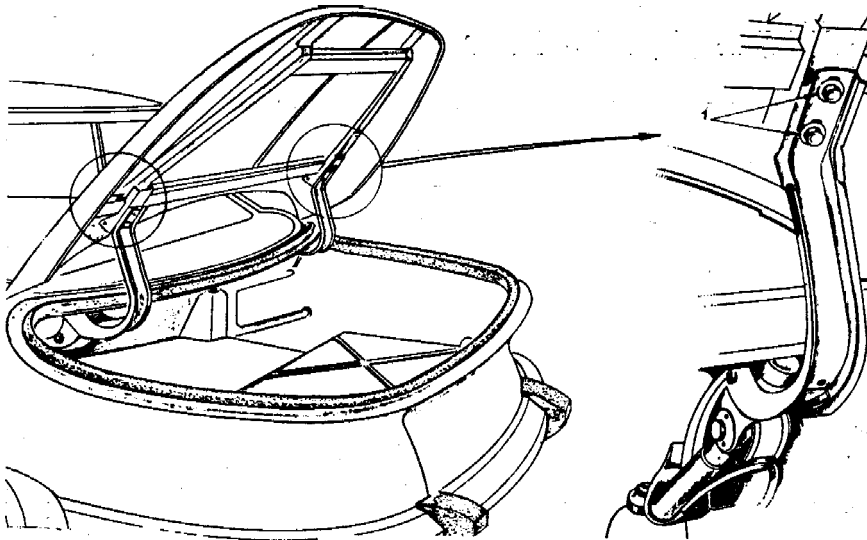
Dépose et repose d'un couvercle de malle. — 1. Vis de réglage.
